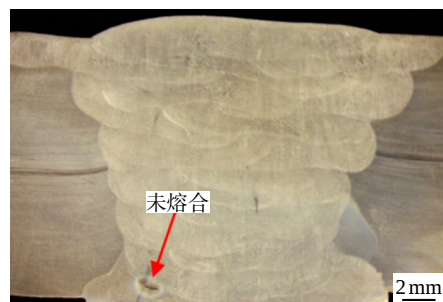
50 mm/min 焊接速度下的焊道形貌
